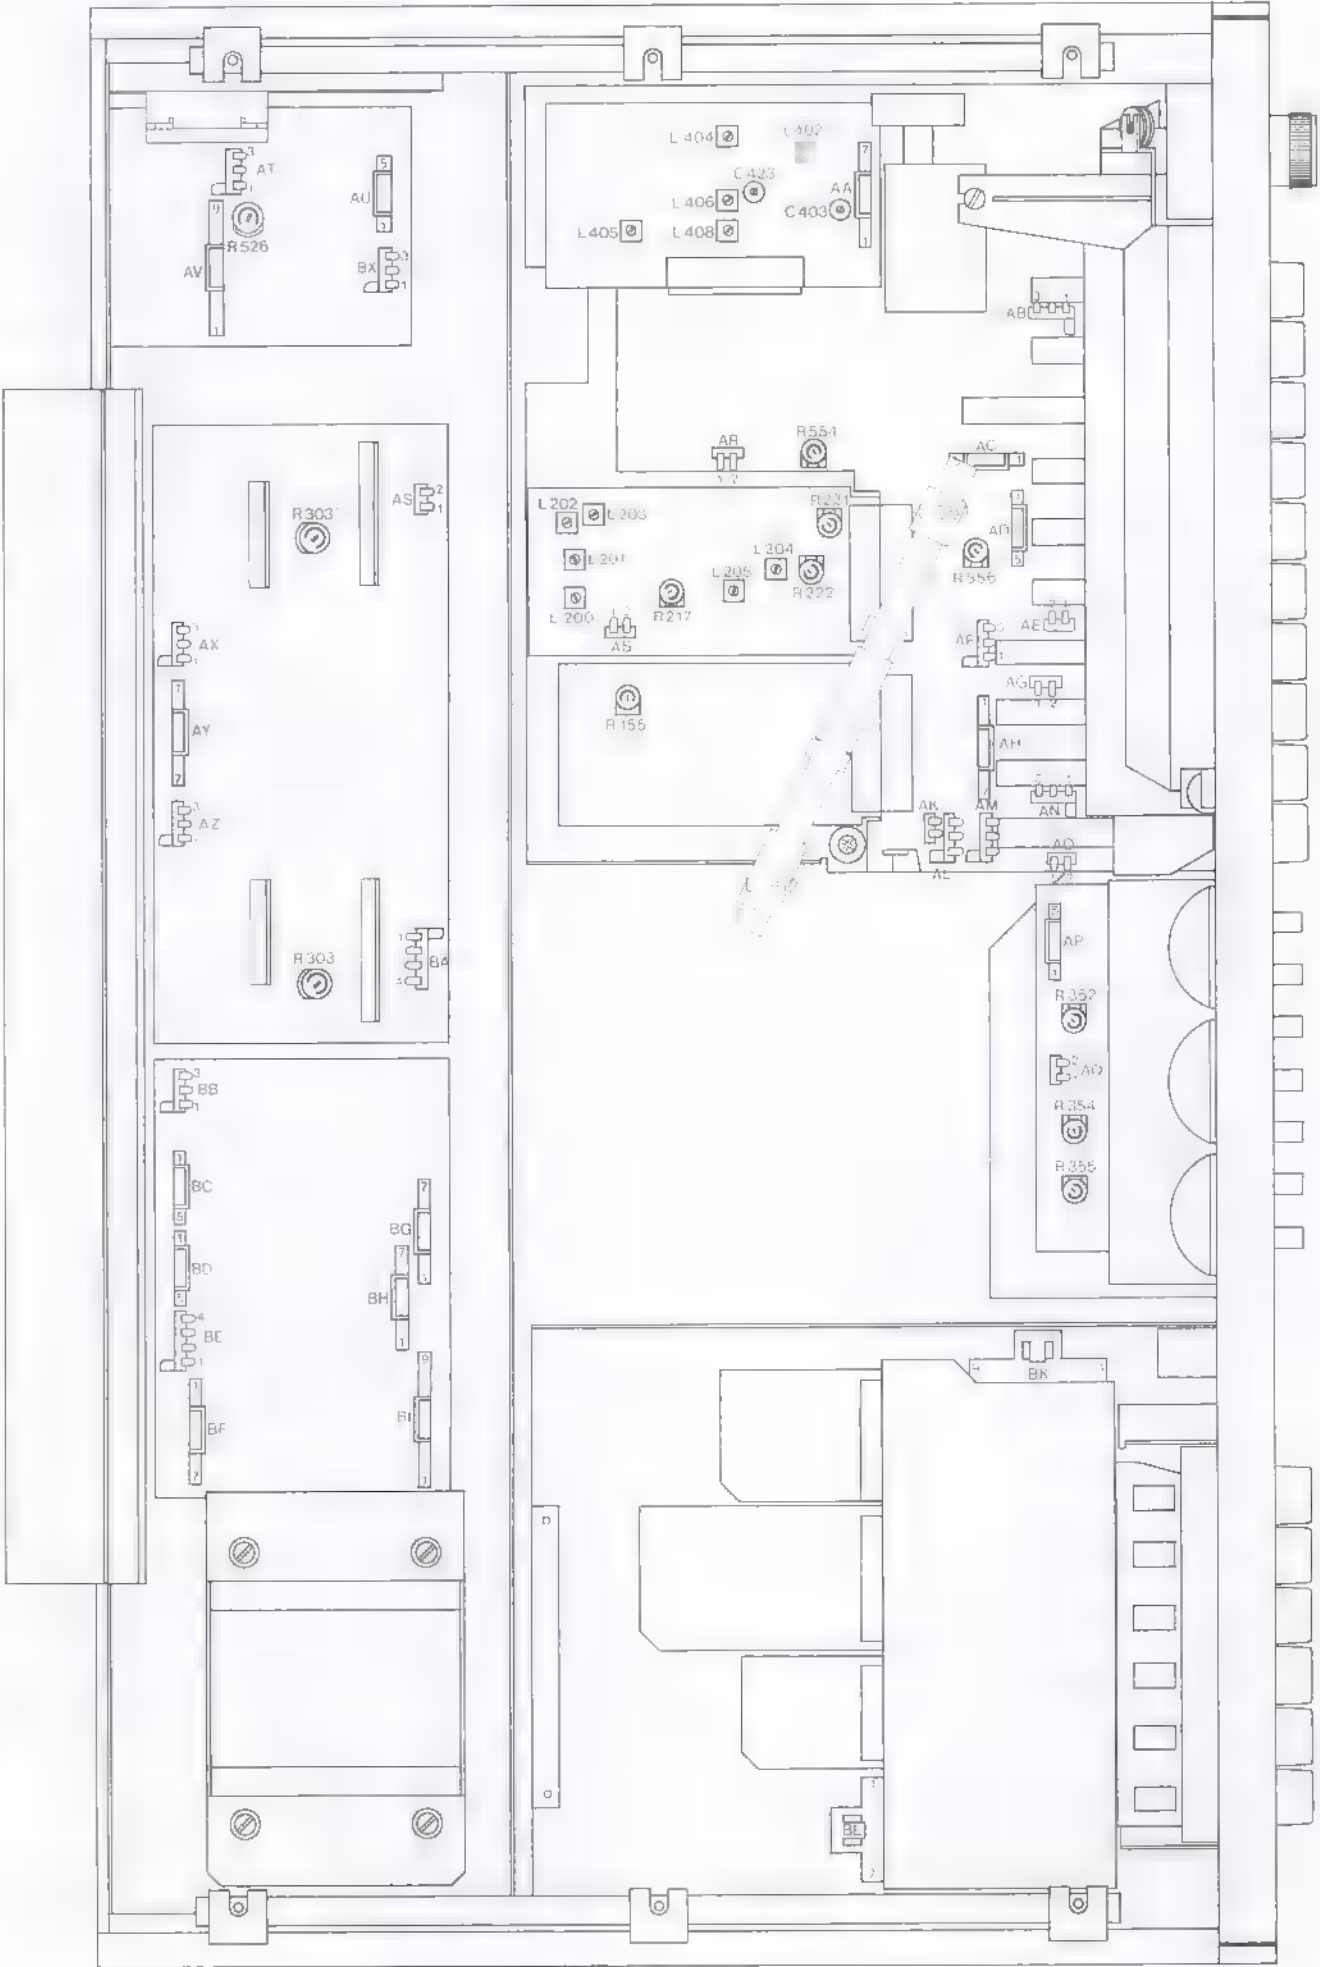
Abgleichpositionen und Lageplan der Steckverbindungen
